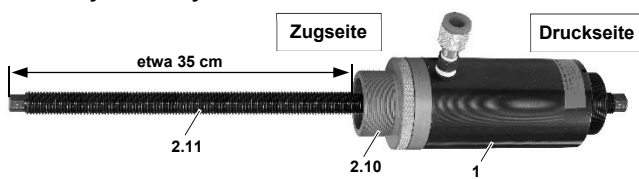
Hydraulik-Zylinder in Grundplatte einschrauben. Spannmutter aufschrauben.
